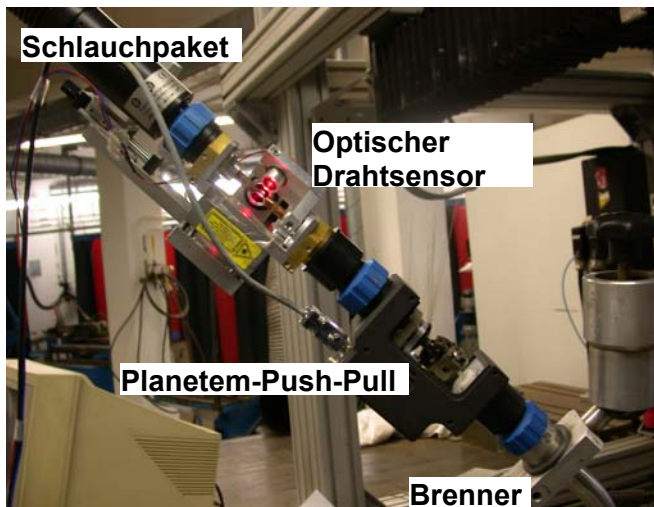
Schweißbrenner mit Planeten-Push-Pull-Antrieb und optischer Drahtgeschwindigkeitsmessung
